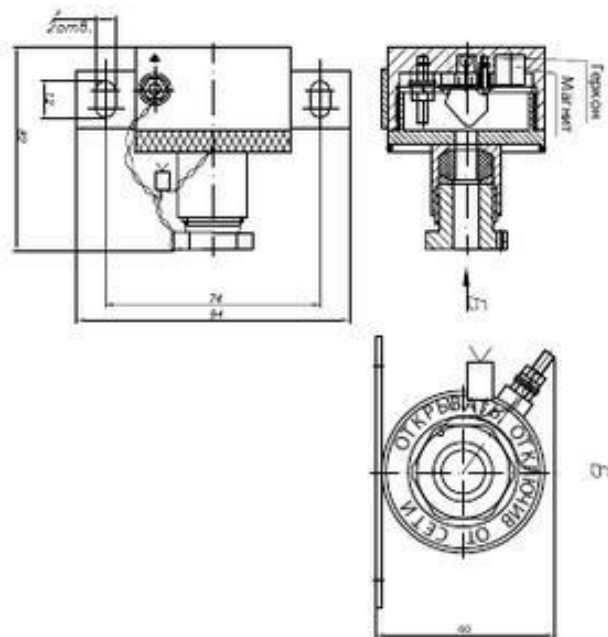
Габаритные и присоединительные размеры МГДУ КП модели 03.
